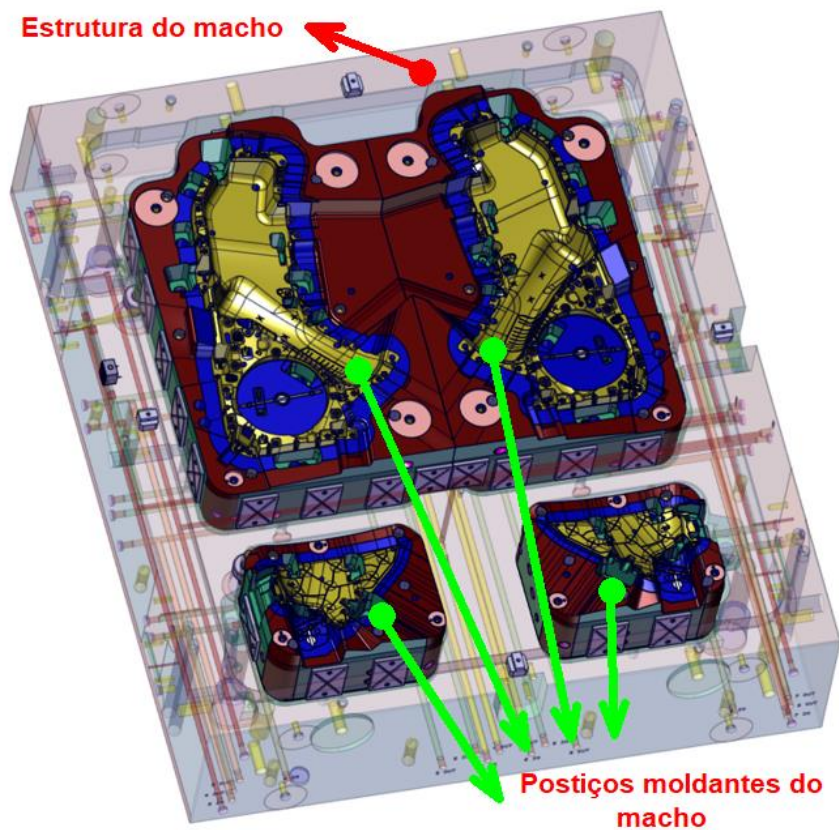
Exemplo da placa de um macho estruturado fabricado na SF Moldes.
